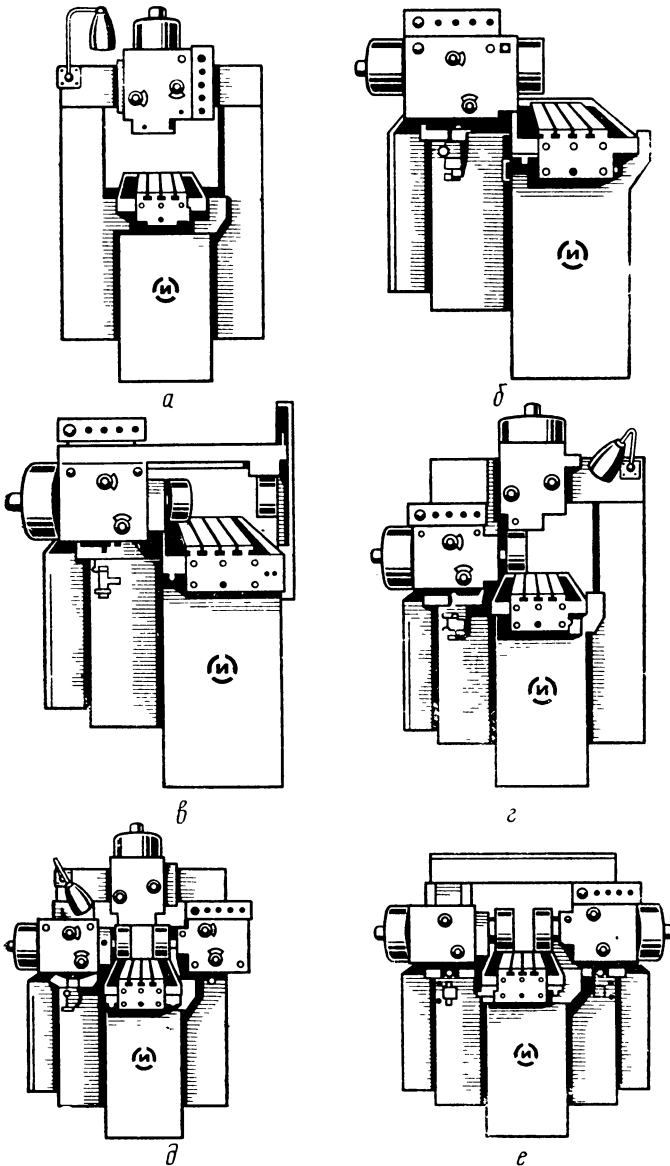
Семейство металлорежущих станков Ленинградского филиала ВНИИТЭ
